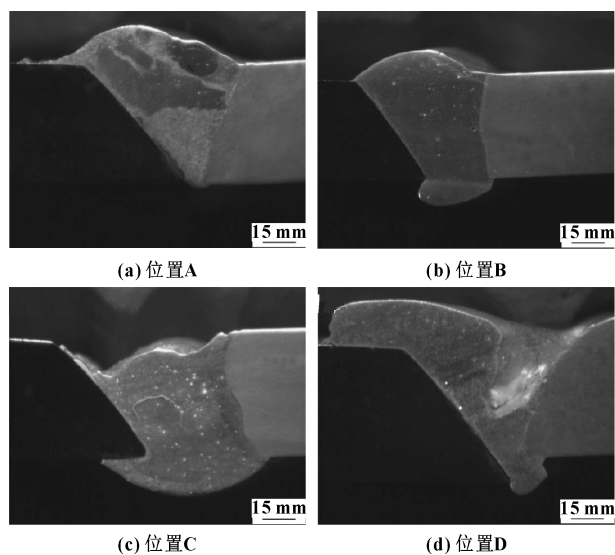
不同焊丝位置对的焊接接头横截面形貌
